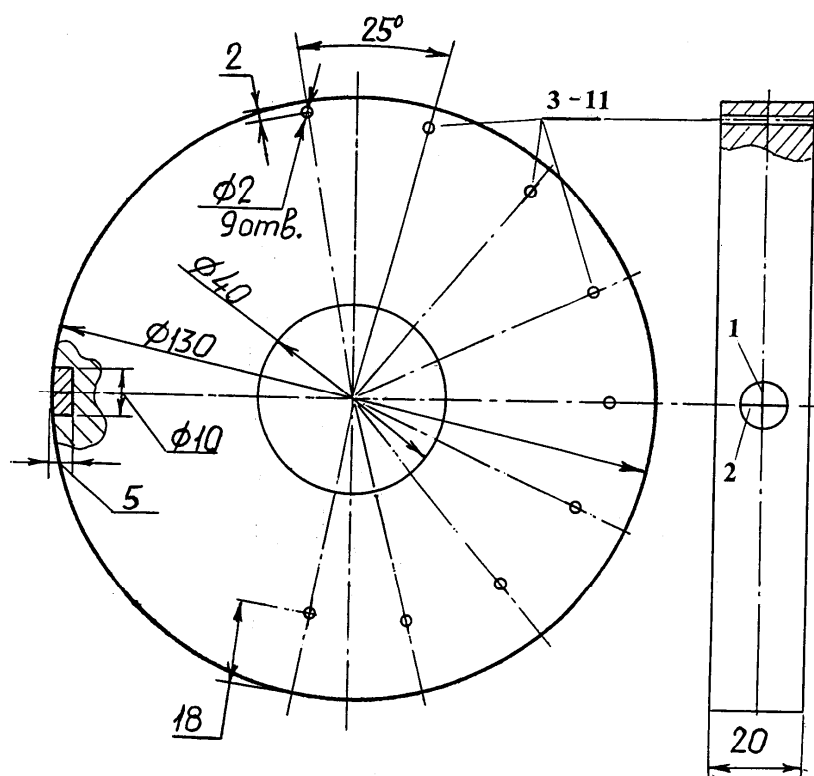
Контрольный образец МО-4 Шелихова Г.С.
